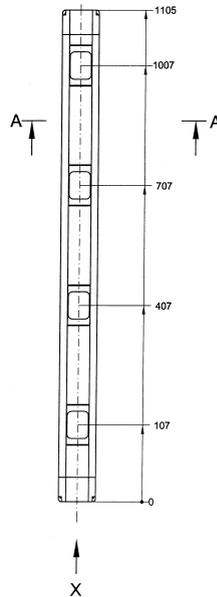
Maßzeichnung Passiver Umlenkspiegel PM4-300 (Zubehör)
